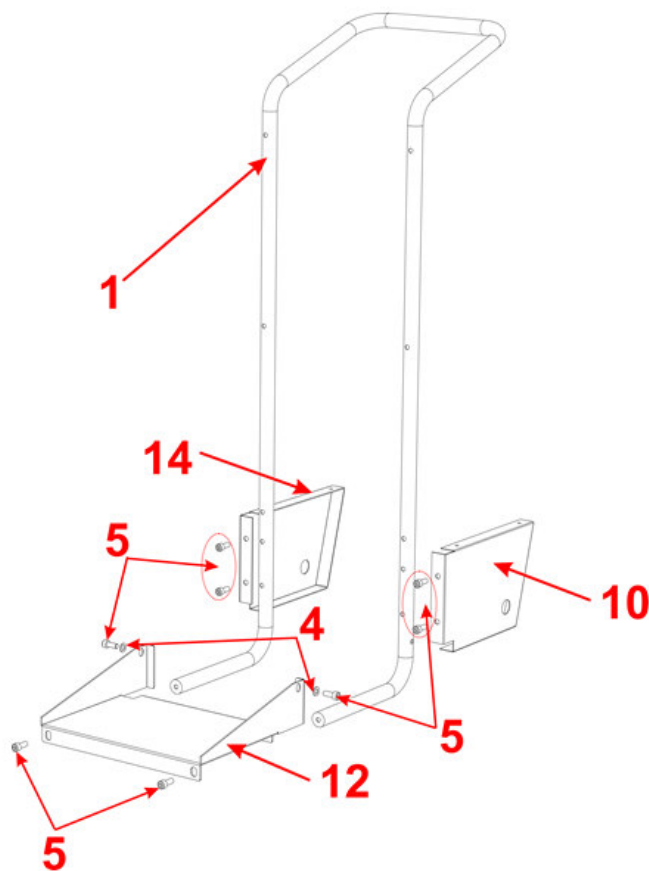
Montage des Schweißgerätwagens Schritt 1
